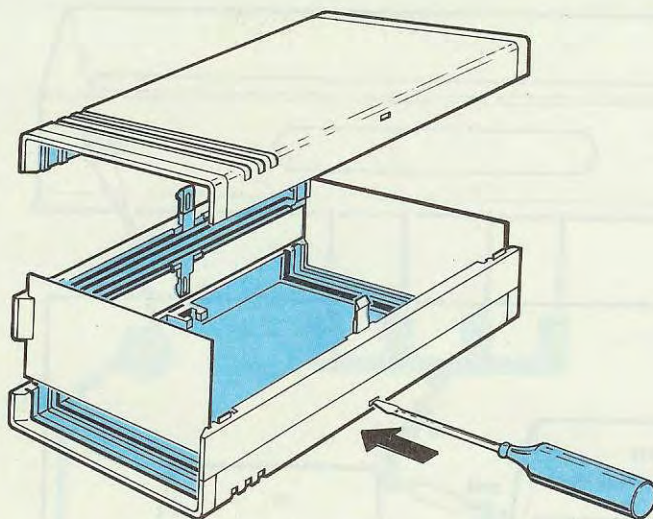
Il mobile per questo ionodepuratore è un modello deluxe di colore grigio perla, provvisto internamente di guide laterali per l'innesto del circuito stampato. Per aprire i due gusci del mobile sarà sufficiente premere all'interno delle due fessure laterali con la lama di un cacciavite per sganciare la levetta del fermo.
